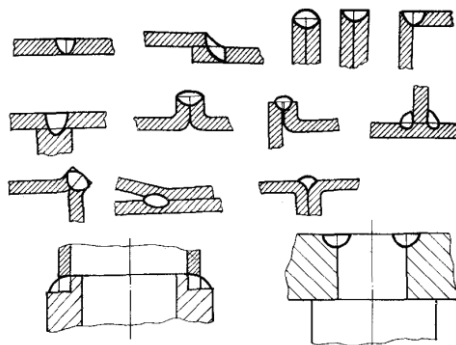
Типы соединений, выполняемых шовной лазерной сваркой
